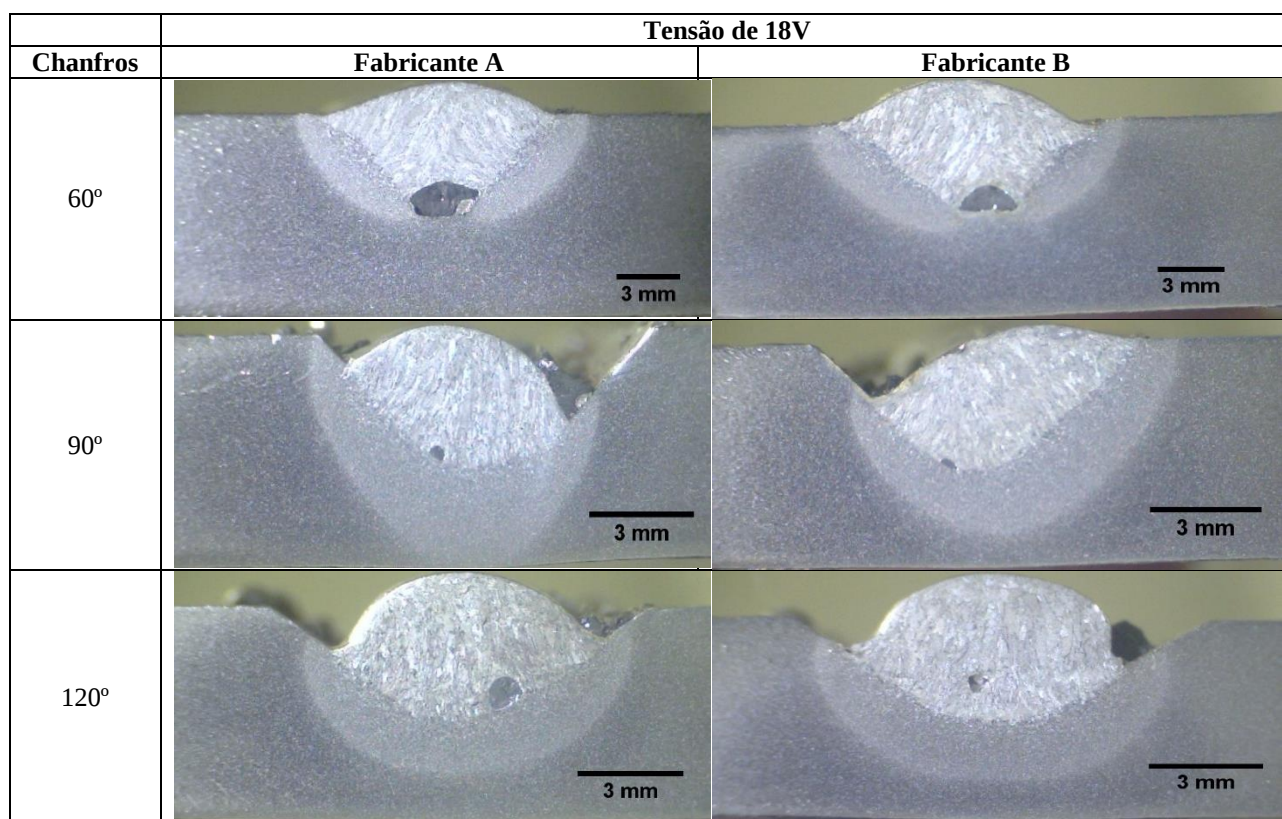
Seção transversal dos cordões de solda com tensão de 18V dos fabricantes A e B.
